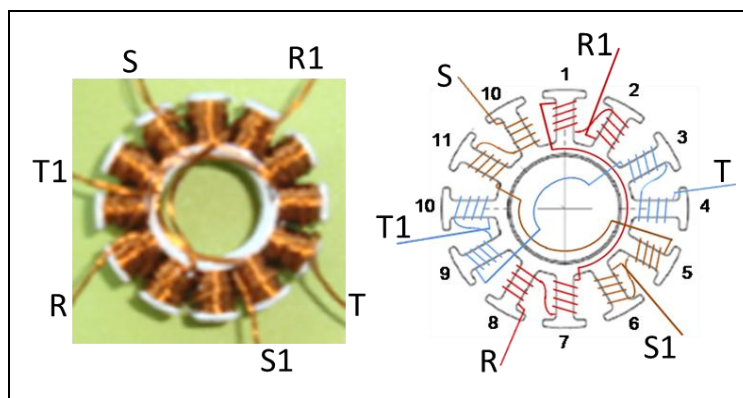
Bobinagem fase T-T1, do estator sinterizado em bloco único de Fe1%P do mini-motor.
